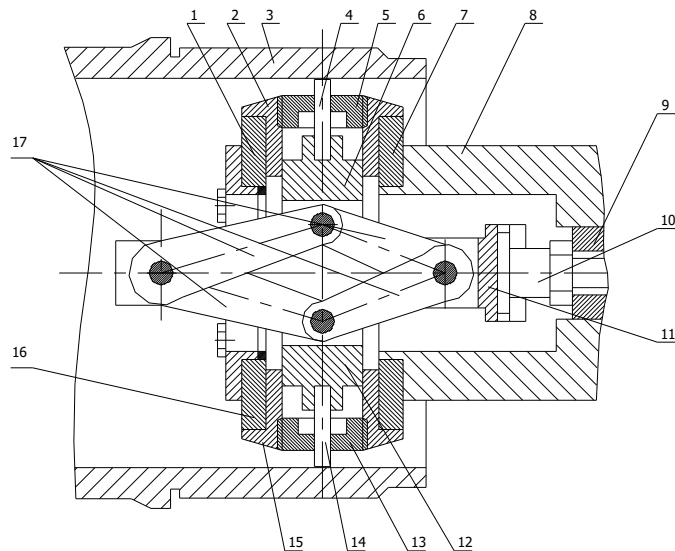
Схема пристрою для ФАБО гільзи циліндра
